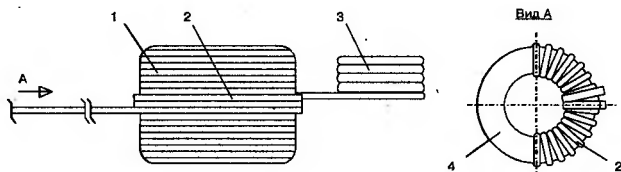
Наматка обмоток сварочного аппарата:
